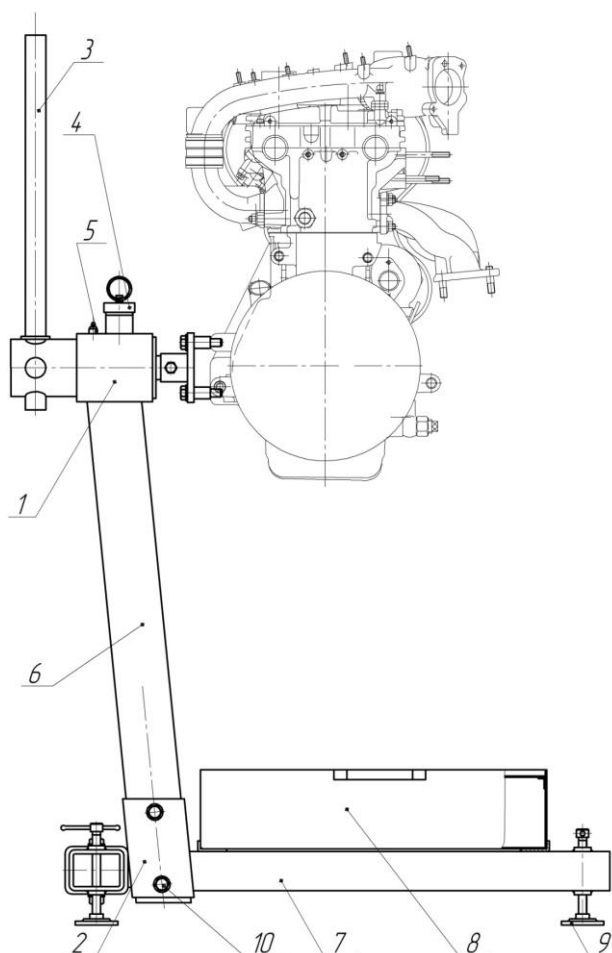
Схема стенда-кантователя для ремонта двигателя
